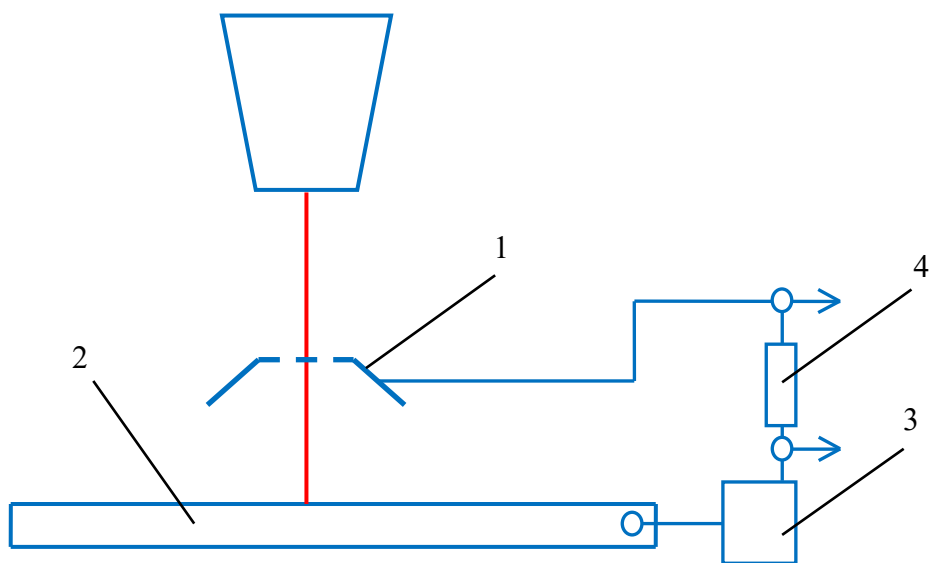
Схема регистрации вторично-эмиссионного тока при лазерной сварке в вакууме: 1 – коллектор заряженных частиц; 2 – свариваемое изделие; 3 – источник напряжения смещения; 4 – резистор нагрузки
